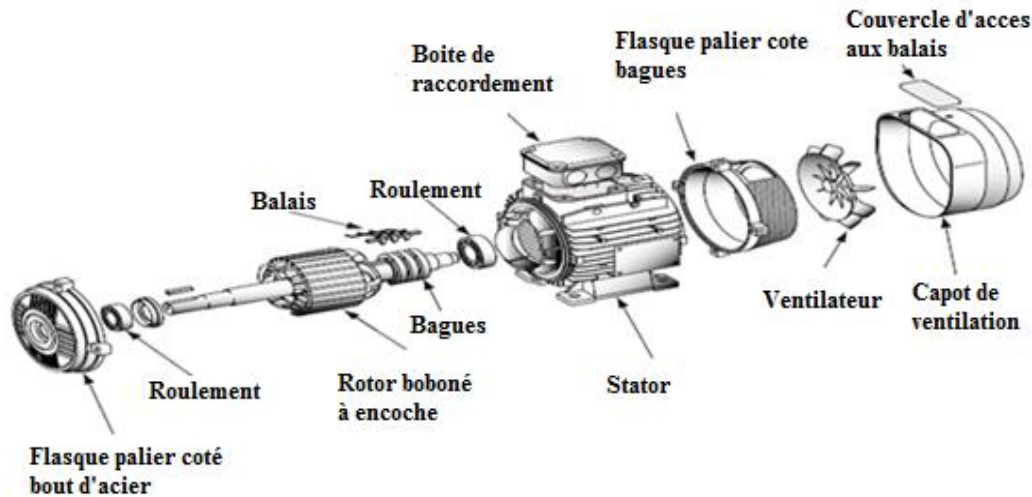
Vue d'un rotor bobiné (à bagues) d'un moteur asynchrone triphasé.
